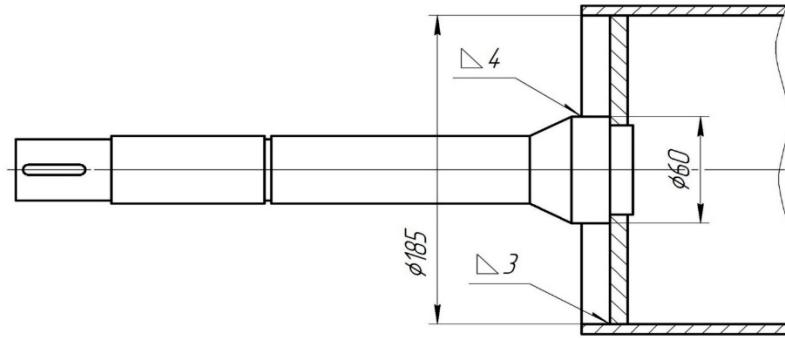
Схема приварки цапфи вала очищувально-передавального вальця
